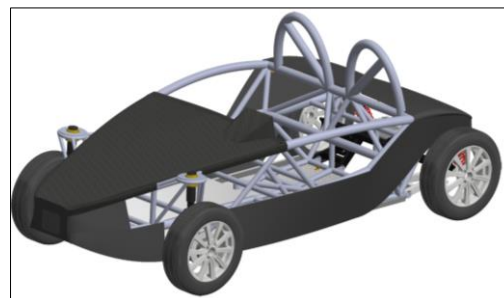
Diseño de los puntos de anclaje del carenado y piso.
